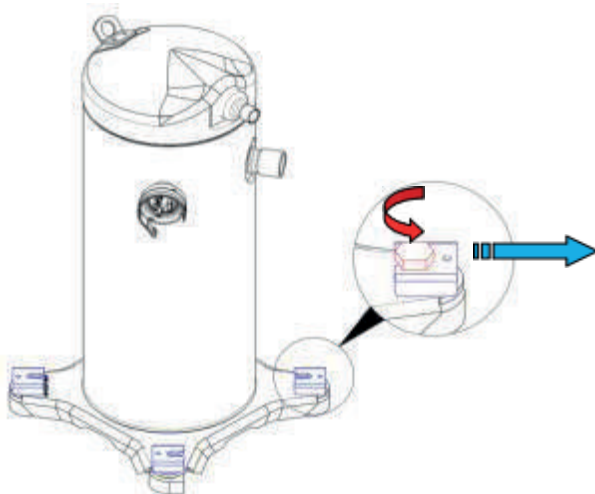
«Снятие транспортировочного крепления компрессора».
